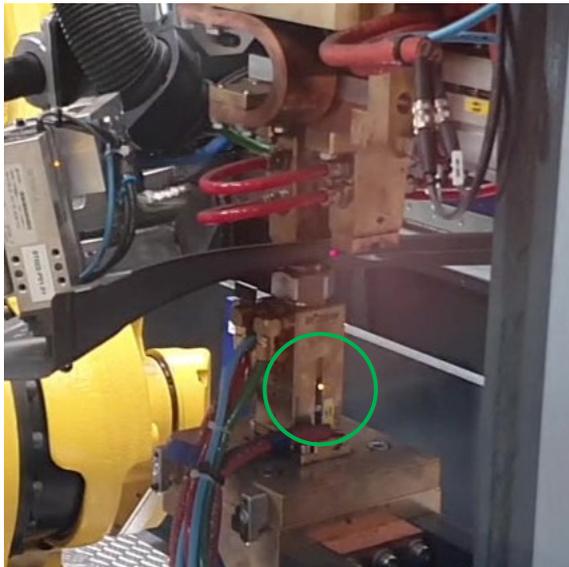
Bauteil in Schweißposition eingelegt → Mutterkontrolle i.O.
